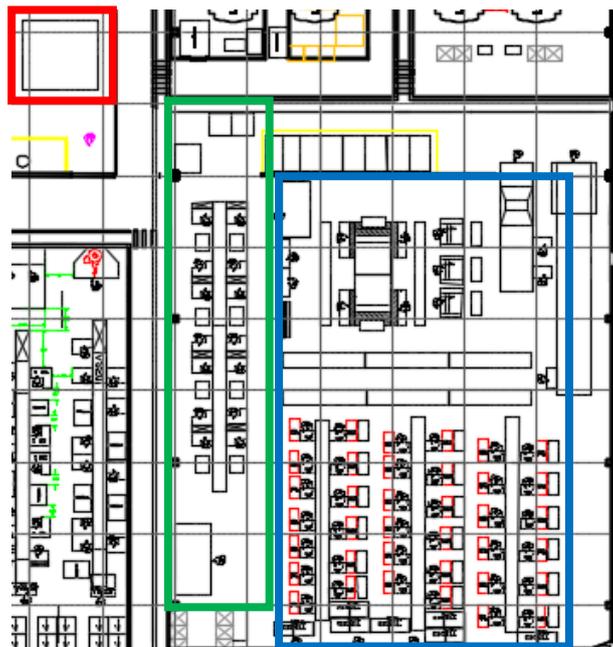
Layout actual de las zonas de cosido y montaje. Fuente: Elaboración propia
